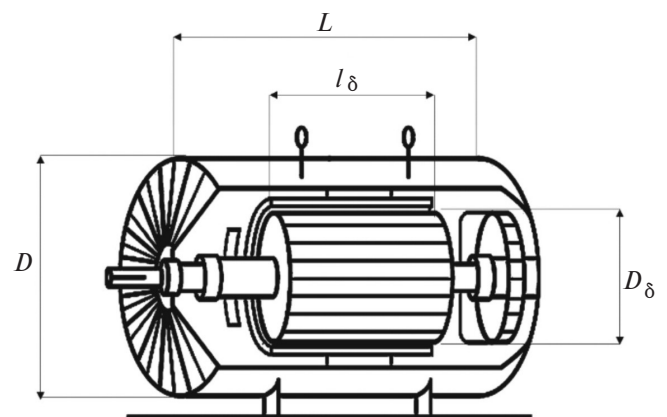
Габаритные размеры электрической машины и размеры ее ротора
